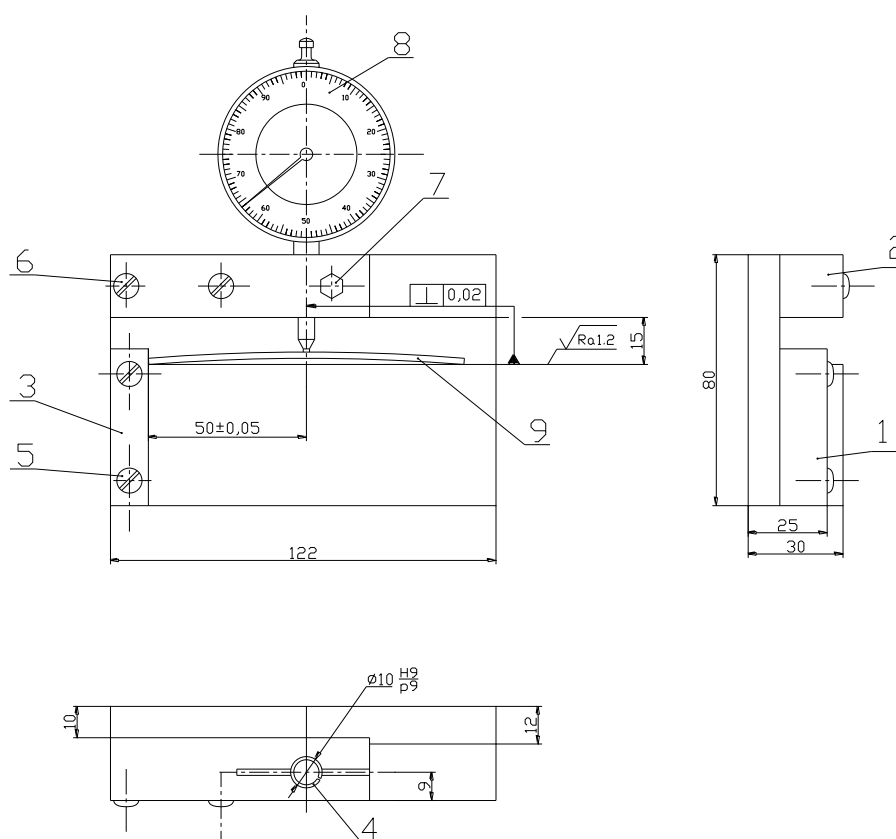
Индикаторное приспособление для измерения контрольных пластинок: 1 – корпус; 2 – зажим; 3 – упор; 4 – втулка; 5 – винт; 6 – винт; 7 – болт; 8 – индикаторная головка, 9 – контрольная пластина
